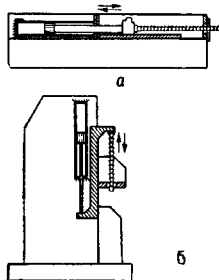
Схемы протяжных станков: а — горизонтального; б — вертикального для внутреннего протягивания.
